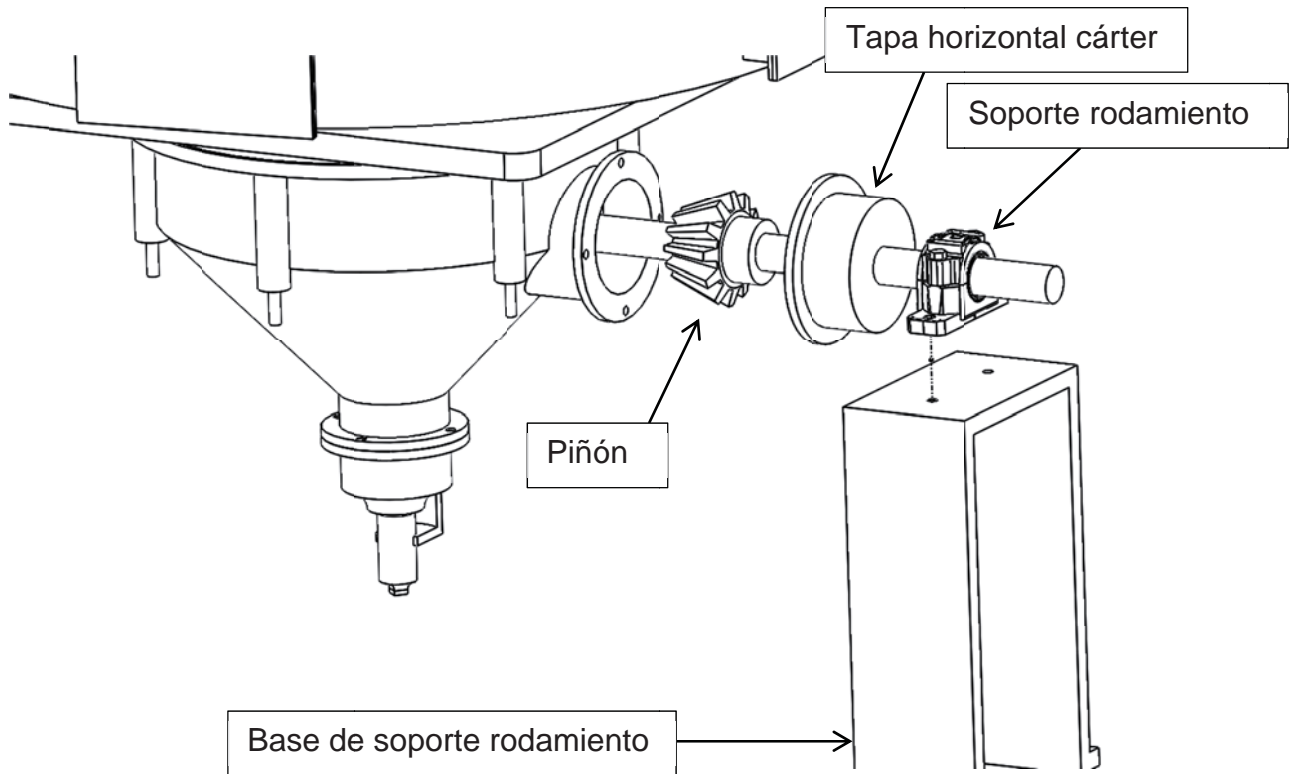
Representación montaje piñón, soporte rodamiento, eje horizontal, etc.
